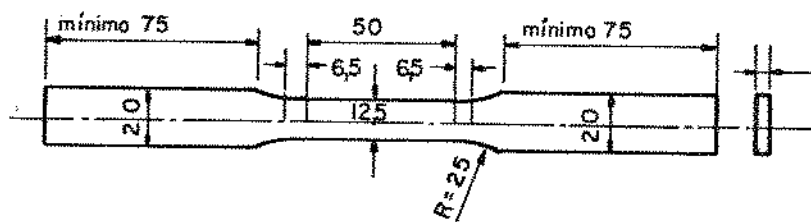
Forma e dimensões (mm) dos CDPs para os ensaios de tração.
